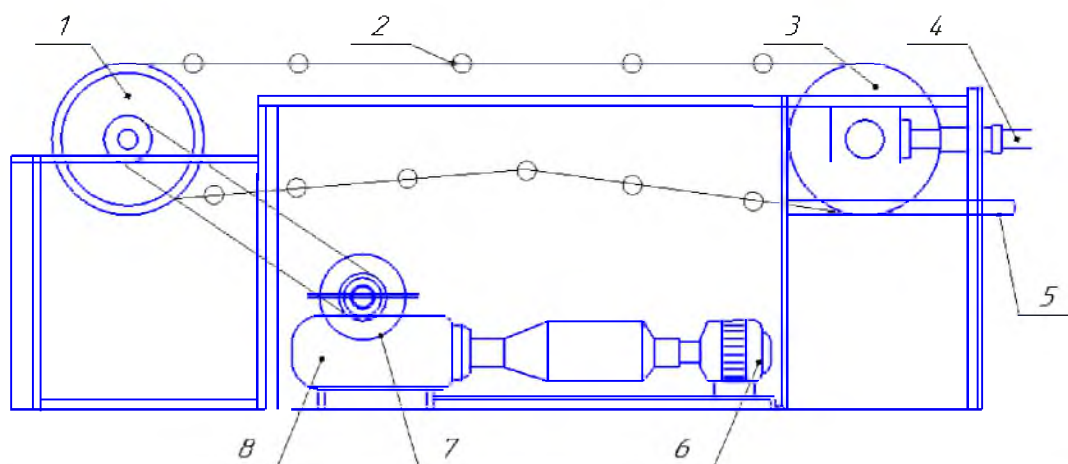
Цепной транспортер: 1 - приводной барабан; 2-цепь; 3 - ведомый натяжной барабан; 4-натяжная станция; 5-станина; 6-электродвигатель; 7-зубчатая передача; 8-редуктор.
